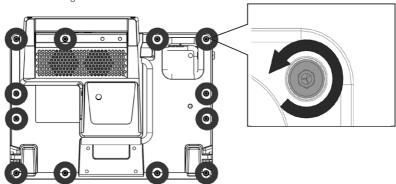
Lösen der Gehäuseschrauben 🛈 , um den Rehadapter™ zu öffnen.
